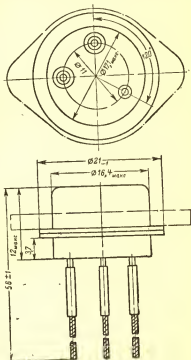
Габаритный чертеж транзисторов П601—П602А.
